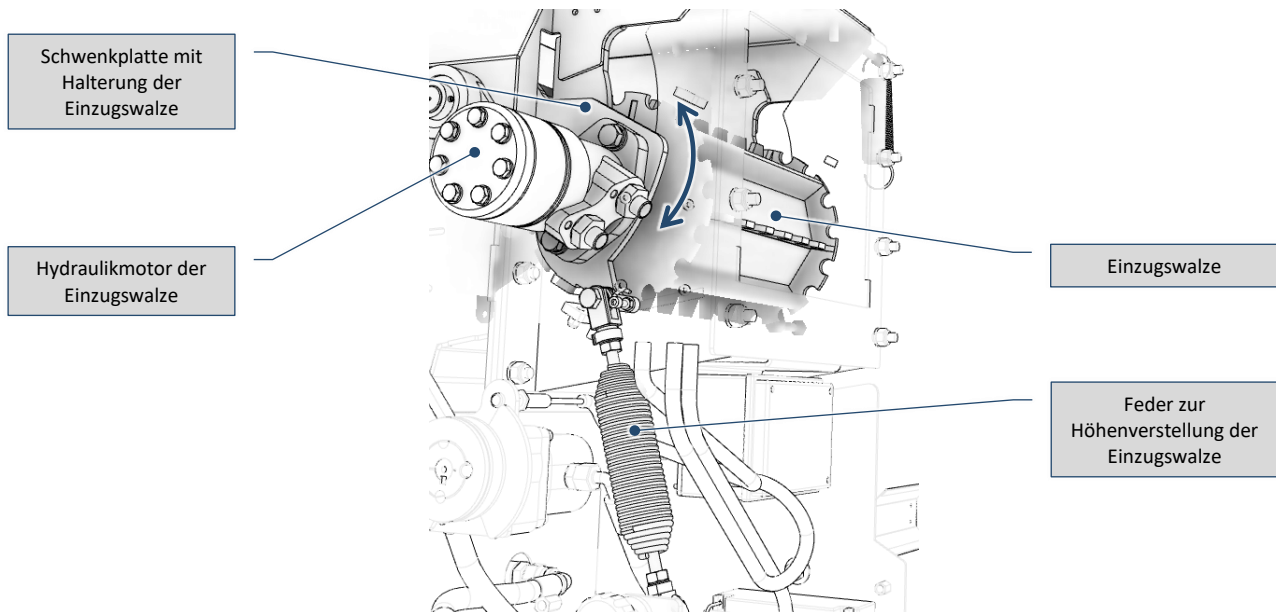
Detail einer der Halterungen der Einzugswalze
